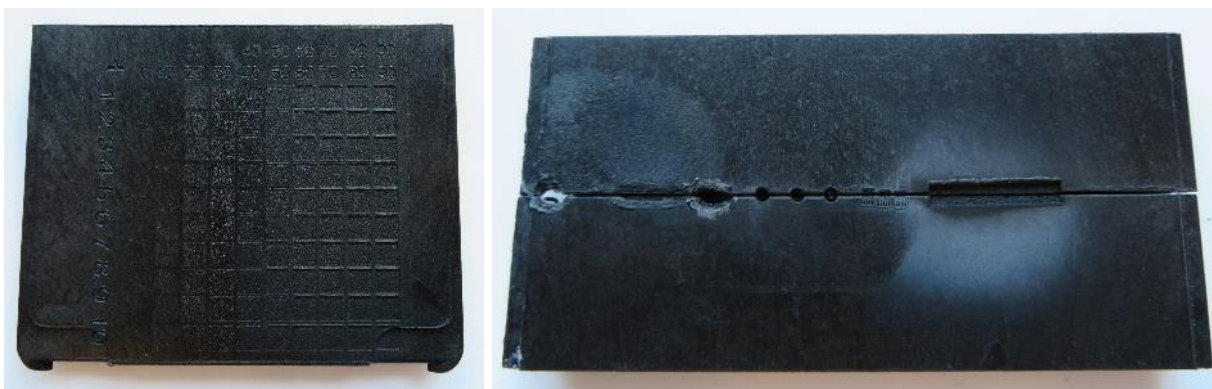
Probekörper gefügt mittels Laserschweißen. Links: Ermittlung der Laserschweißparameter. Rechts: Gefügte Probekörper.
